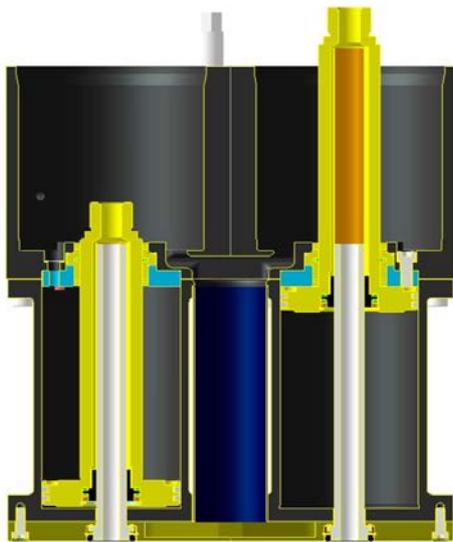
6 ¼ DG Pegelmechanismus auf TG Grundplatte mit PPC Sensoren
